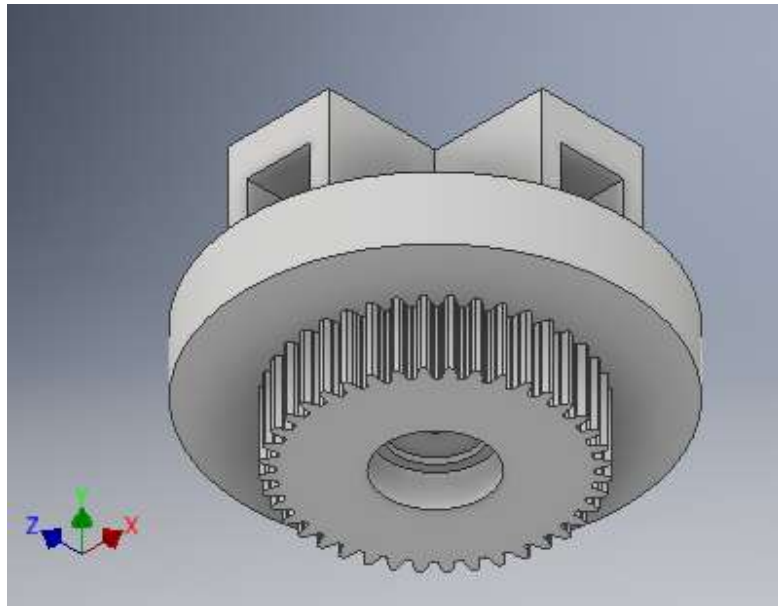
Vista isométrica inferior de la pieza rotor.
